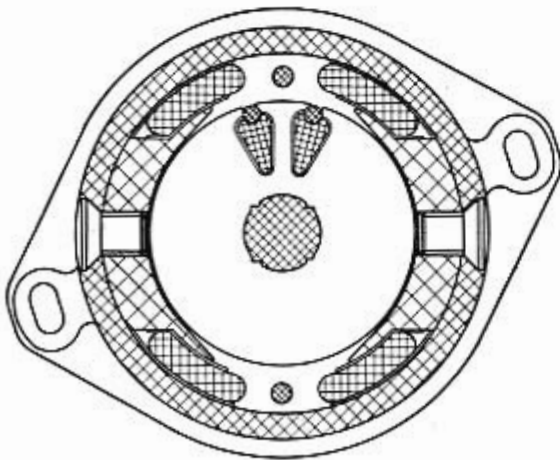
Coupe transversale sur les enroulements, sur les épanouissements polaires et sur la carcasse.
